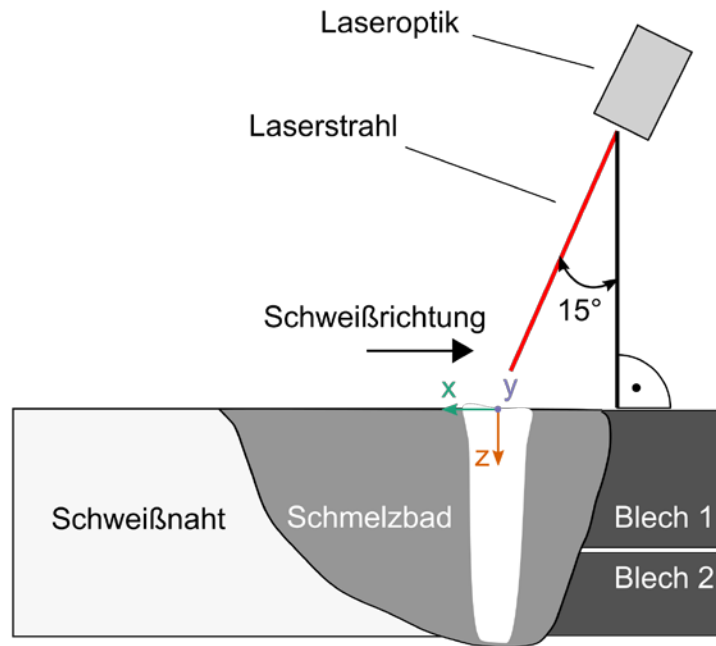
Experimenteller Aufbau der durchgeführten Versuche ist dargestellt. Die Laseroptik ist um circa 15° in Schweißrichtung gekippt, um stechend zu schweißen.
